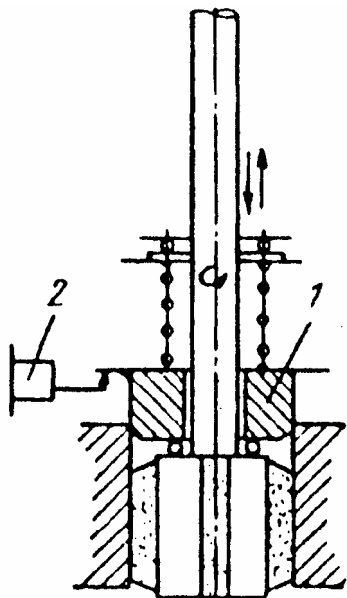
Схема устройства для контроля размеров при хонинговании: 1 – жесткий калибр; 2 – электроконтактный преобразователь
